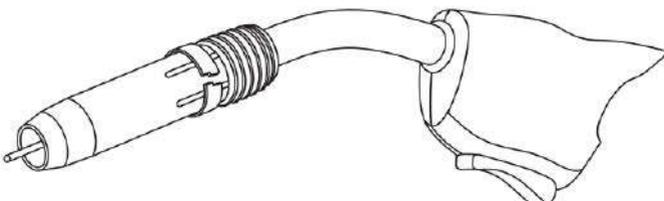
Порядок заправки сварочной проволоки.
